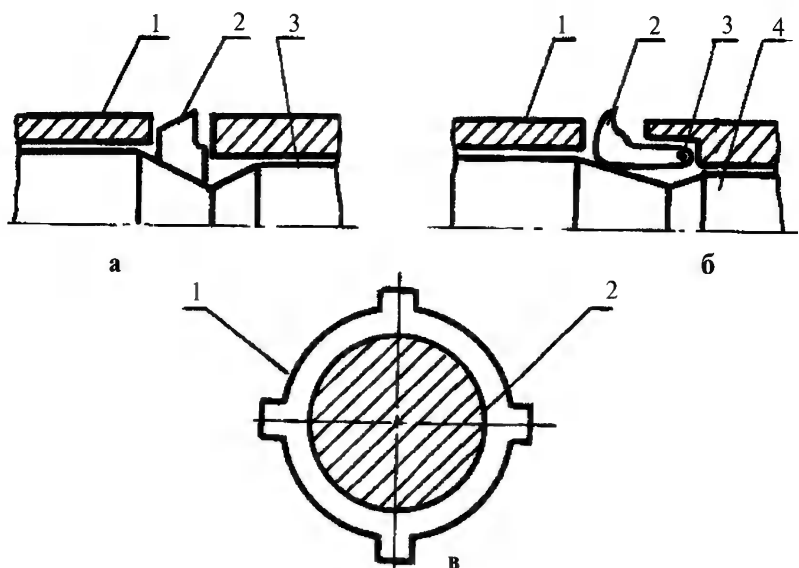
Конструктивные схемы нарезательных головок: а - с радиальным выдвижением резцов (1 - корпус, 2 - резец, 3 - клин), б - с круговым выдвижением резцов (1 - корпус, 2 - резец, 3 - ось, 4 - клин), в - с дисковыми резцами (1 - резец, 2 - стержень)
